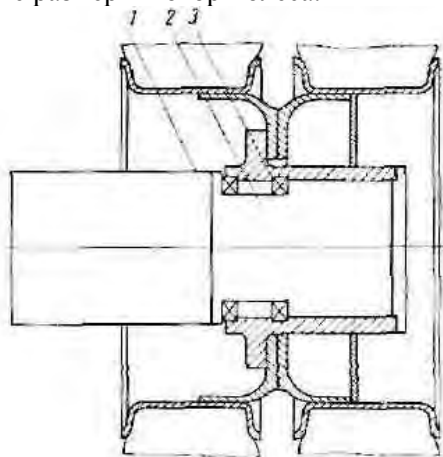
Схема мотор-колеса при компоновке III вида
